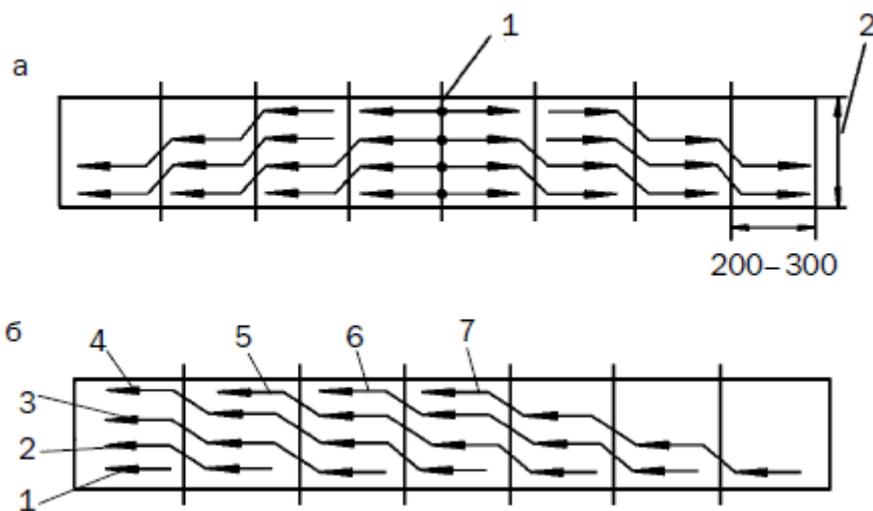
Очередность наложения швов при многослойной дуговой сварке (размеры указаны в миллиметрах): а – горкой; 1 – ось «горки»; 2 – толщина металла; б – каскадом
